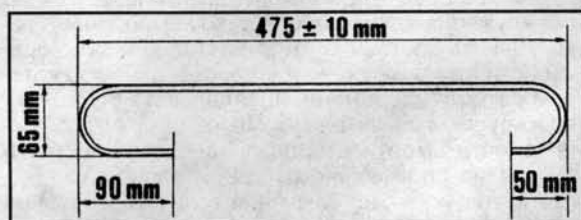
Размеры проволочного крючка диаметром 6 мм для подвешивания элементов подвески переднего колеса при разборке
